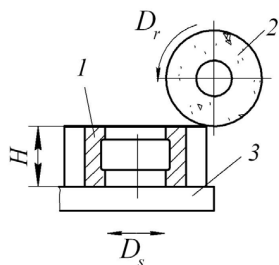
Шлифование базовой поверхности инструмента насадного класса на плоскошлифовальном станке: 1 – заготовка; 2 – шлифовальный круг; 3 – магнитная плита
